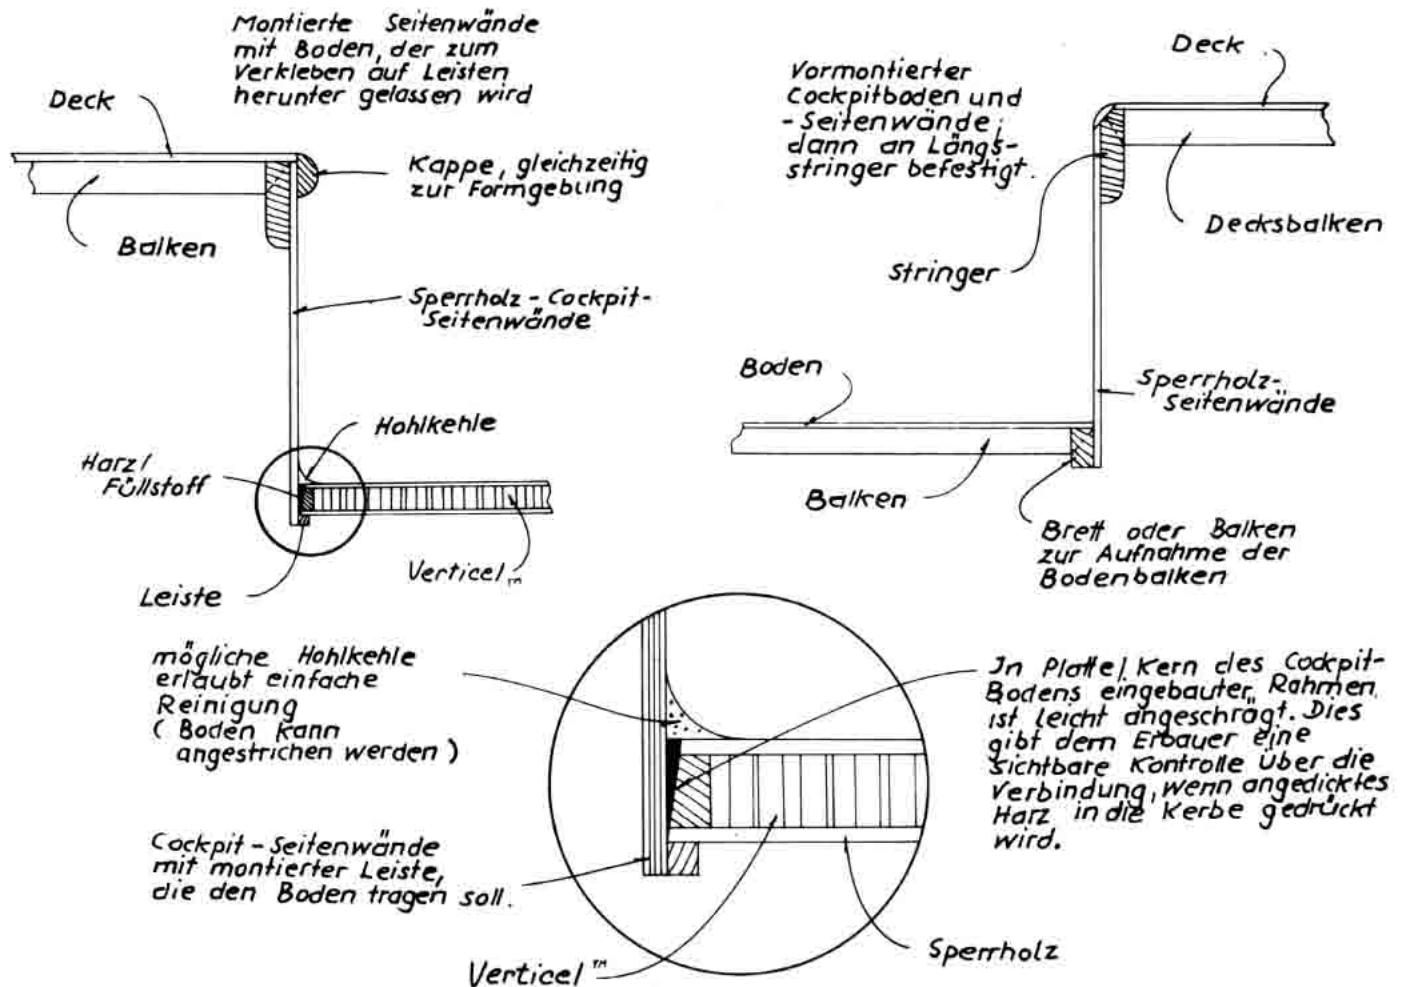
Konstruktionsdetails eines Cockpits.
